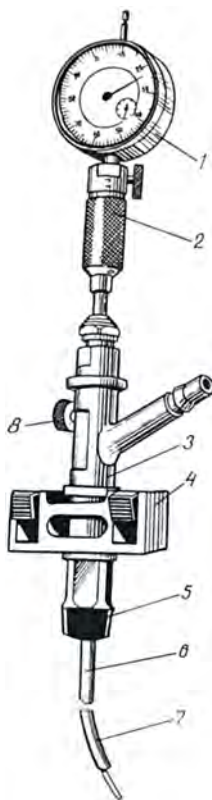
Устройство КИ-11140 ГОСНИТИ для измерения зазоров в КШМ:
